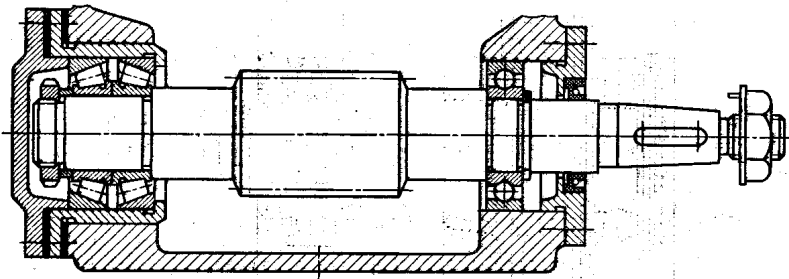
Червячный вал установлен на двух конических роликоподшипниках; правый подшипник — «плавающий» (радиальный однорядный)
